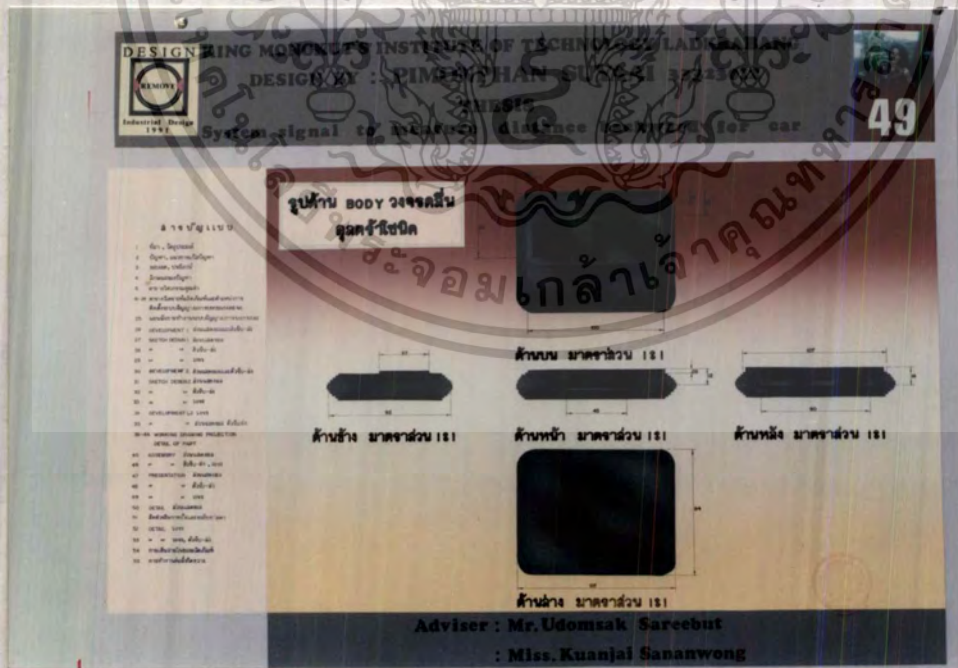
WORKING DRAWING / DETAIL OF PART
